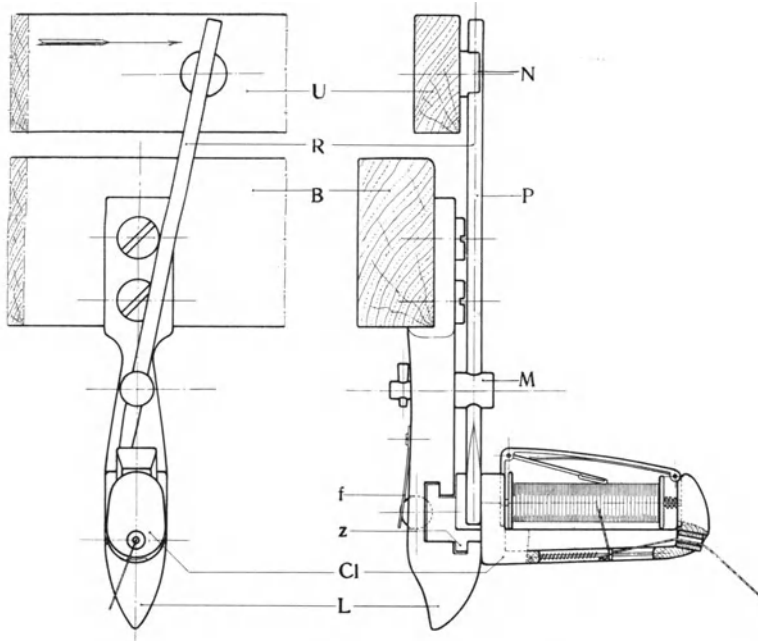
Die h6lzerne Schweizer Broschierlade.
